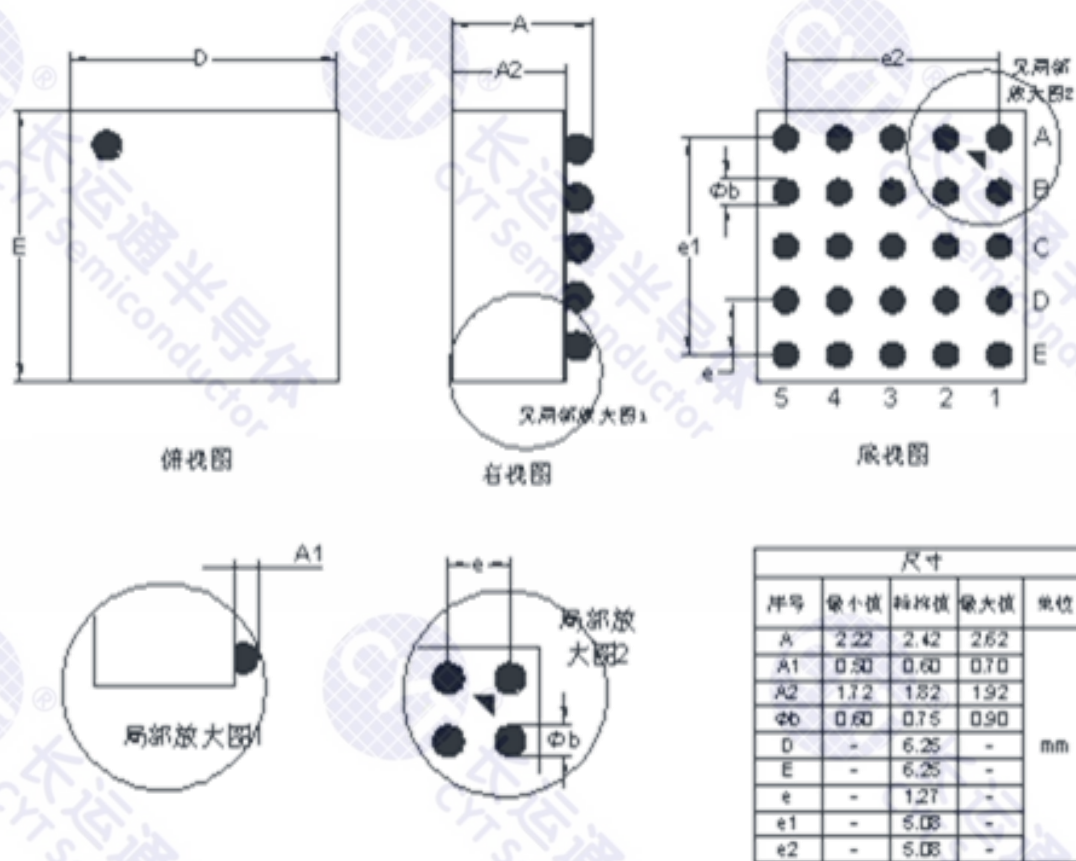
外形尺寸图(6.25mm×6.25mm×2.42mm BGA25)
